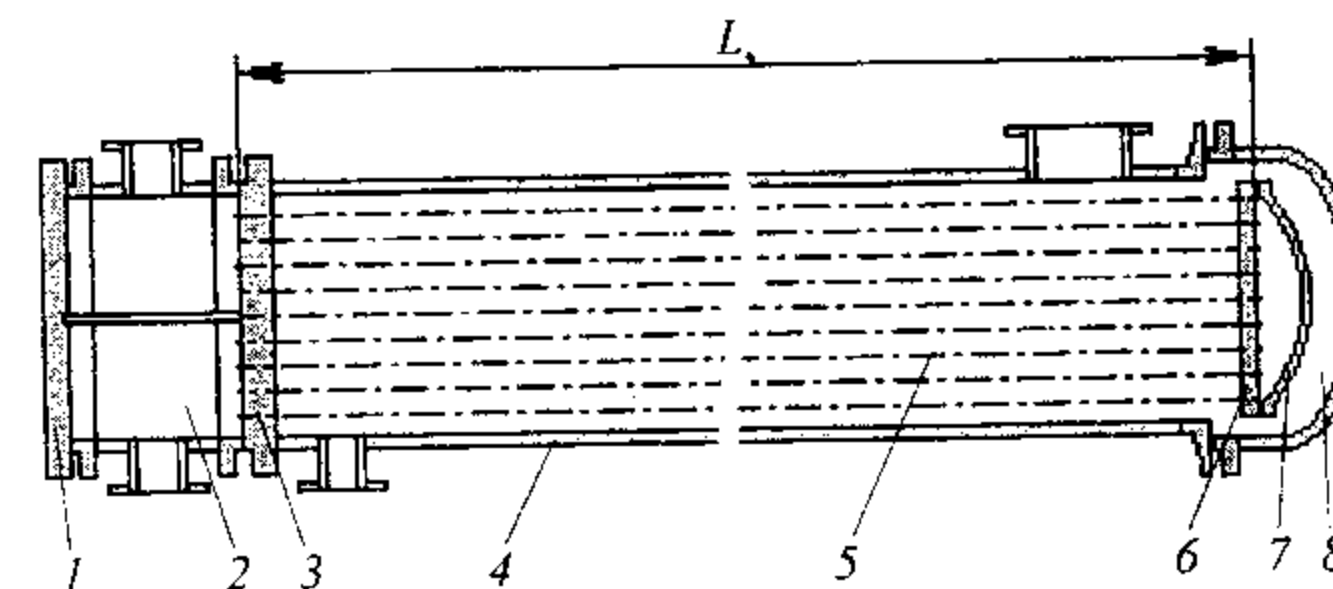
Кожухотрубчатый конденсатор с плавающей головкой: 1 – крышка распределительной камеры; 2 – распределительная камера; 3 – неподвижная трубная решётка; 4 – кожух; 5 – теплообменные трубы; 6 – подвижная трубная решётка; 7 – крышка плавающей головки; 8 – крышка кожуха
